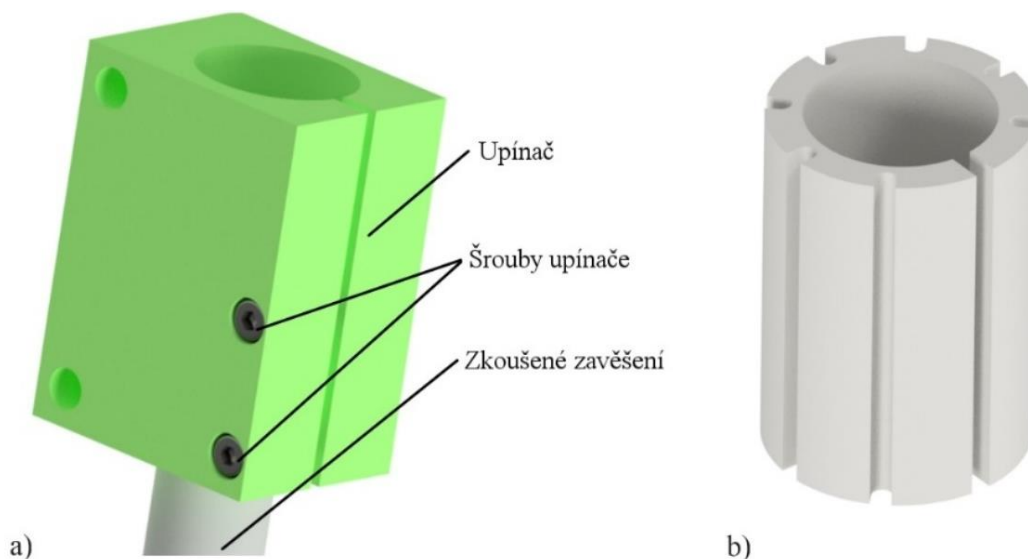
Horní uložení pro testování nosníků motocyklů
